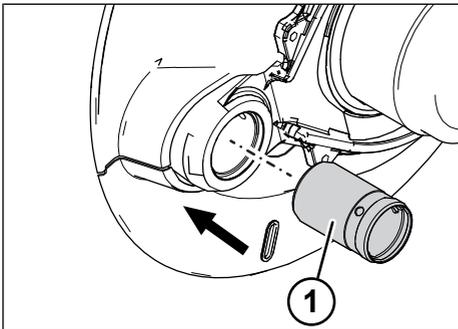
Colocar el casquillo del rodamiento de levas portapastillas
